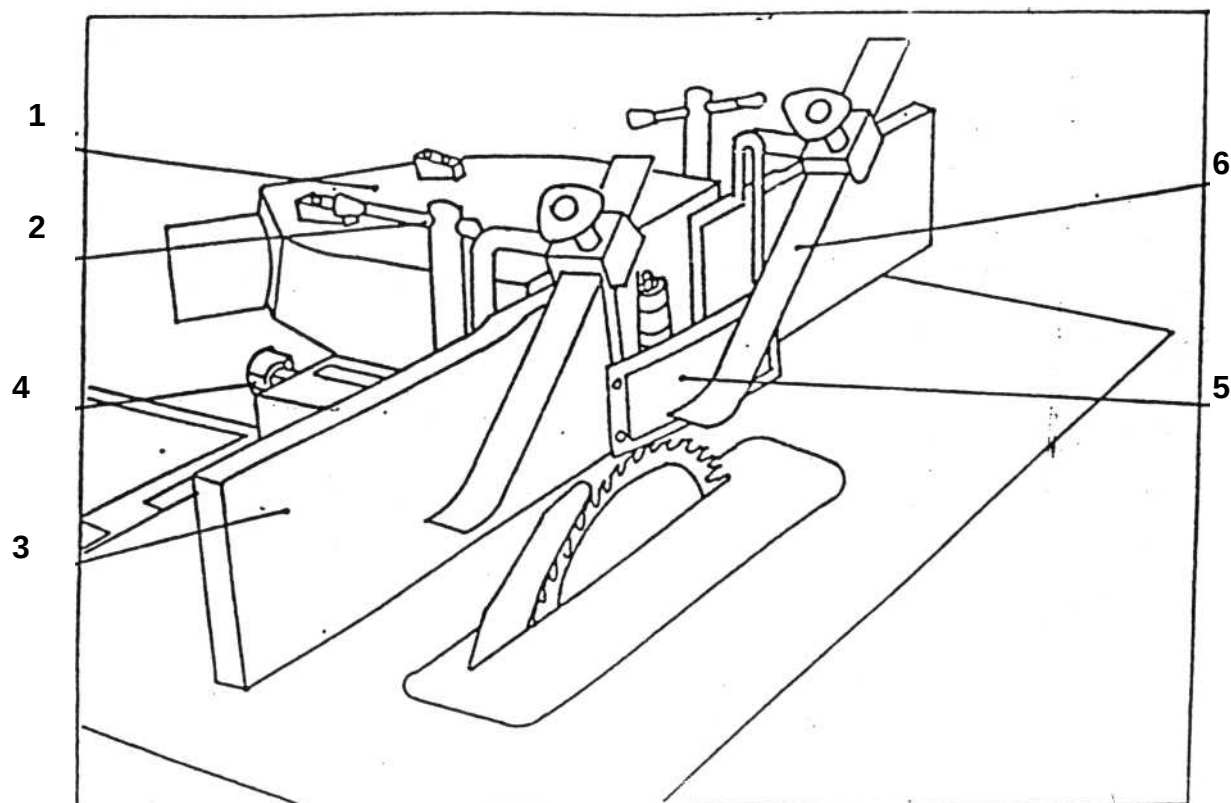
МОНТАЖ ЗАЩИТЫ ФРЕЗЕРНОГО УЗЛА
